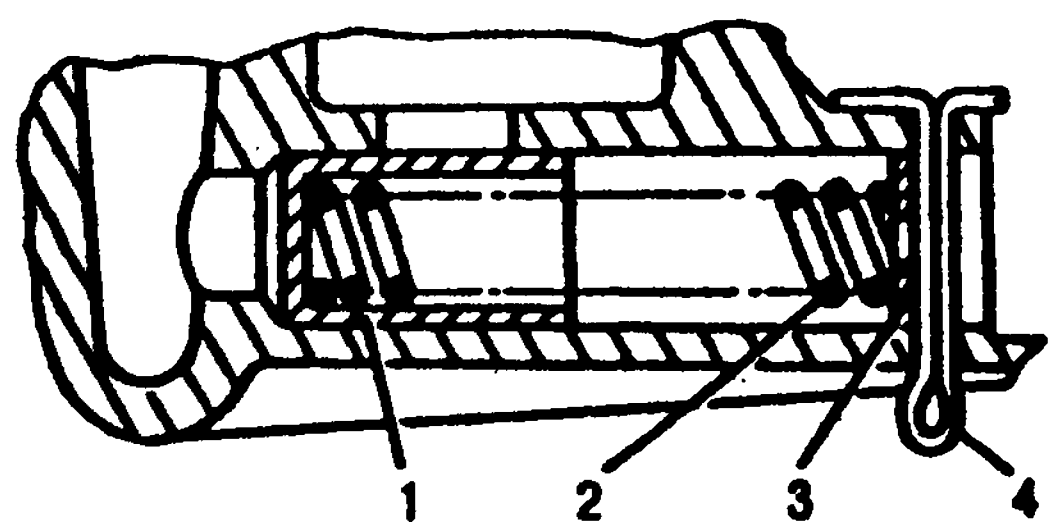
Редукционный клапан: 1 - плунжер; 2 - пружина; 3 - шайба; 4 - шплинт
